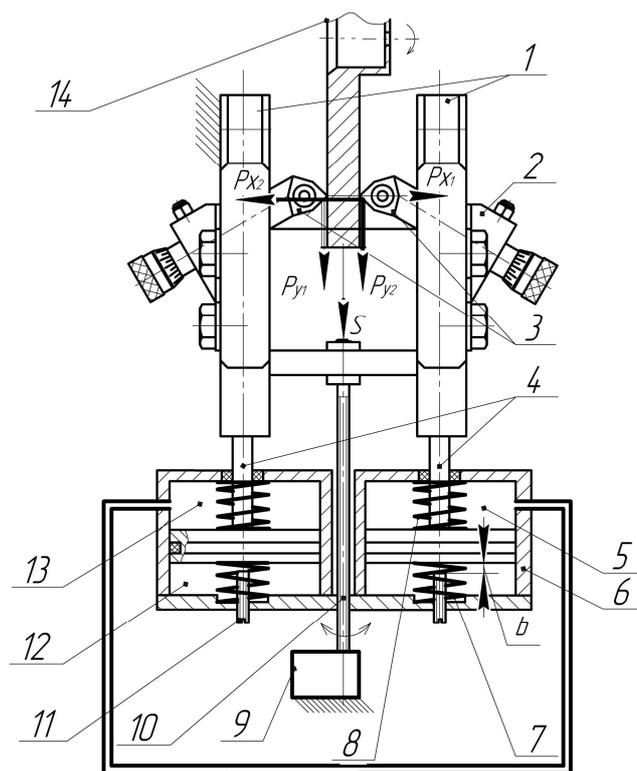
Установка для обработки рабочих поверхностей тормозного диска:
